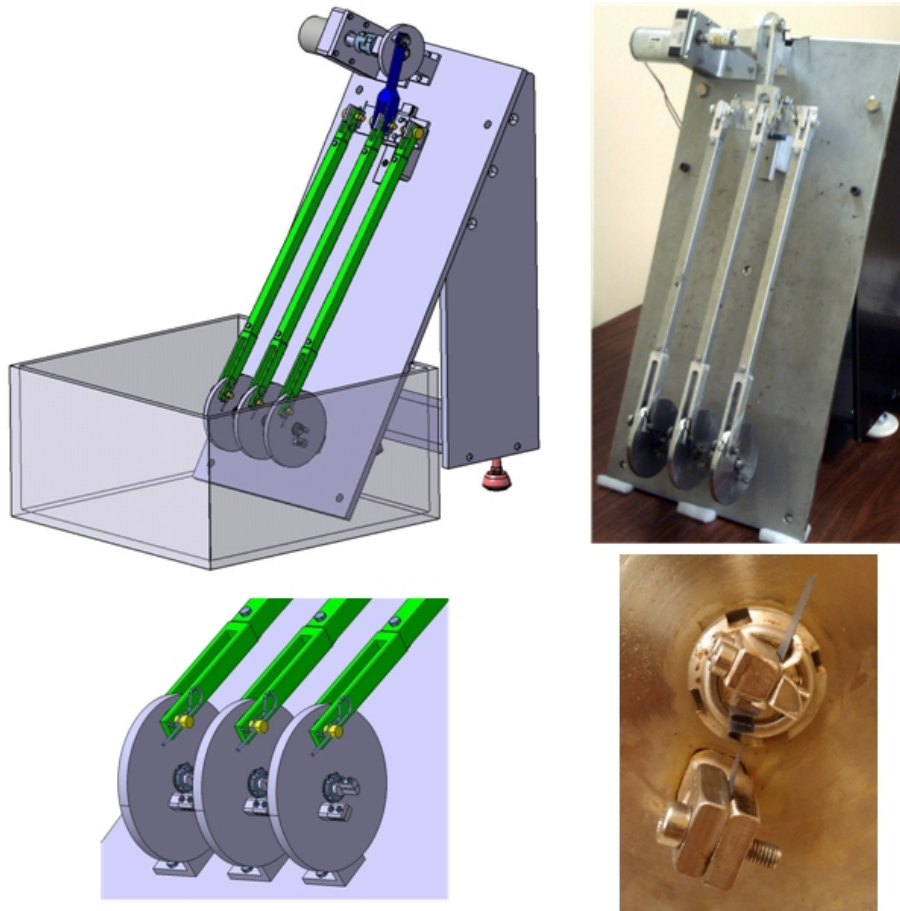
Aperçu de la machine de fatigue développée pour les essais de fatigue des charnières
